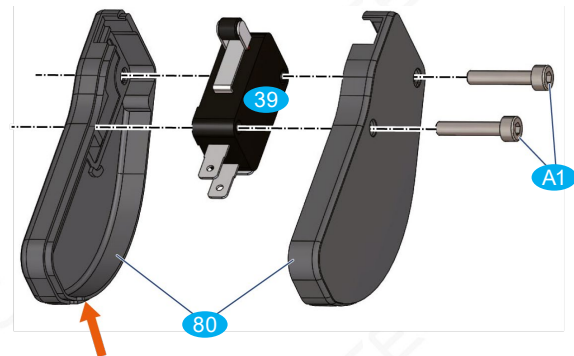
Gehäuse mit Referenzschalter. Der rote Pfeil kennzeichnet die Aussparung zur Kabeldurchführung
